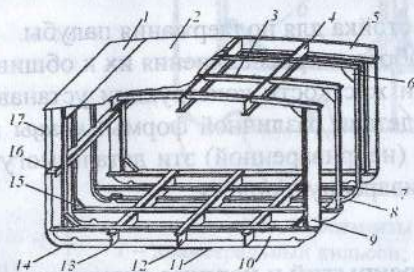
Конструкция корпуса с поперечной системой набора:
